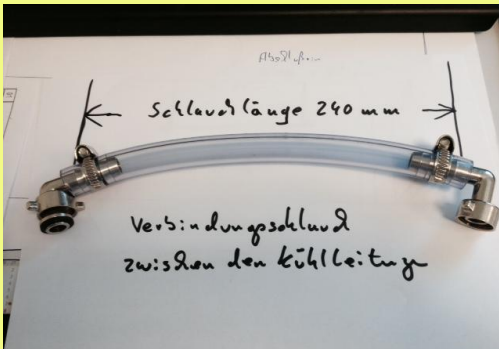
Kühlwasserverbinder bestehend aus 1 Stück PVC-Schlauch, 2 Stück abgewinkelter Schlauchtülle mit Überwurfmutter und 2 Schlauchschellen in fertig montiertem Zustand
